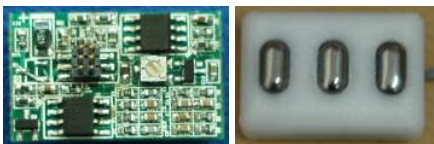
제작된 회로부 PCB 와 조립된 근전위 센서
